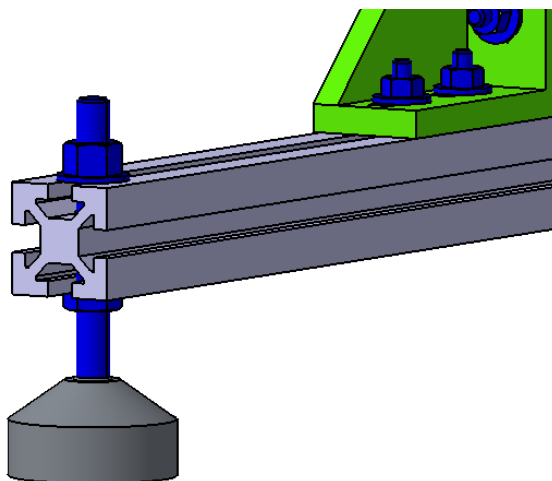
Montaje del soporte anti-vibratorio sobre el perfil de base horizontal
